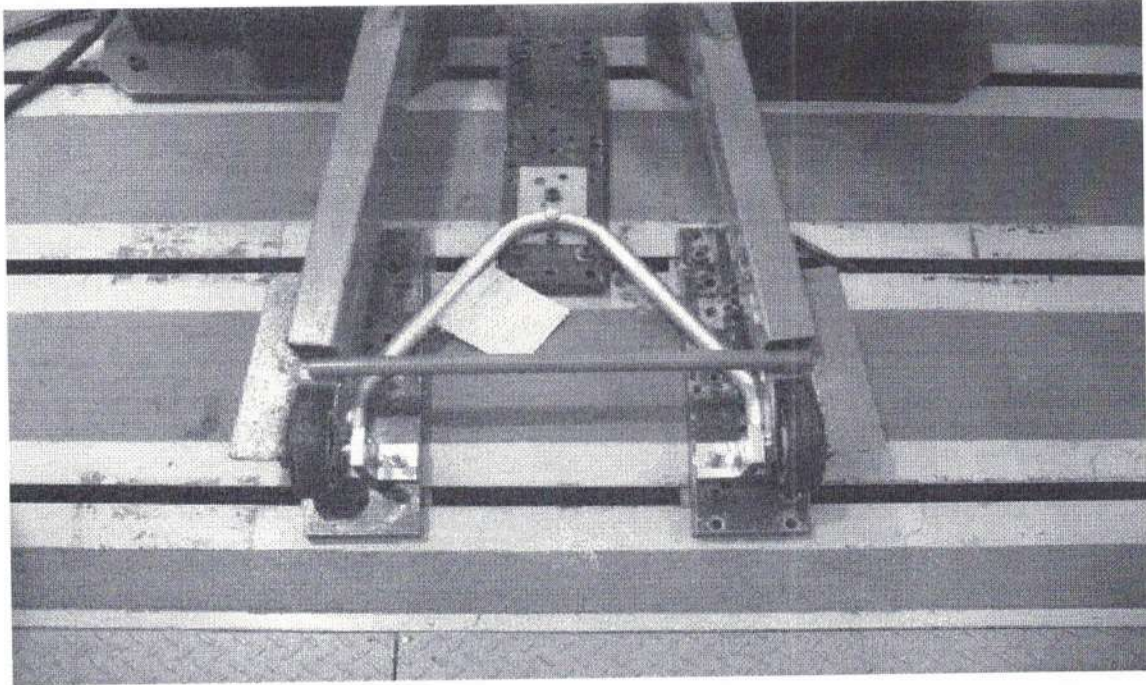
Foto 1 Visão geral amostra 1 após ensaio.
